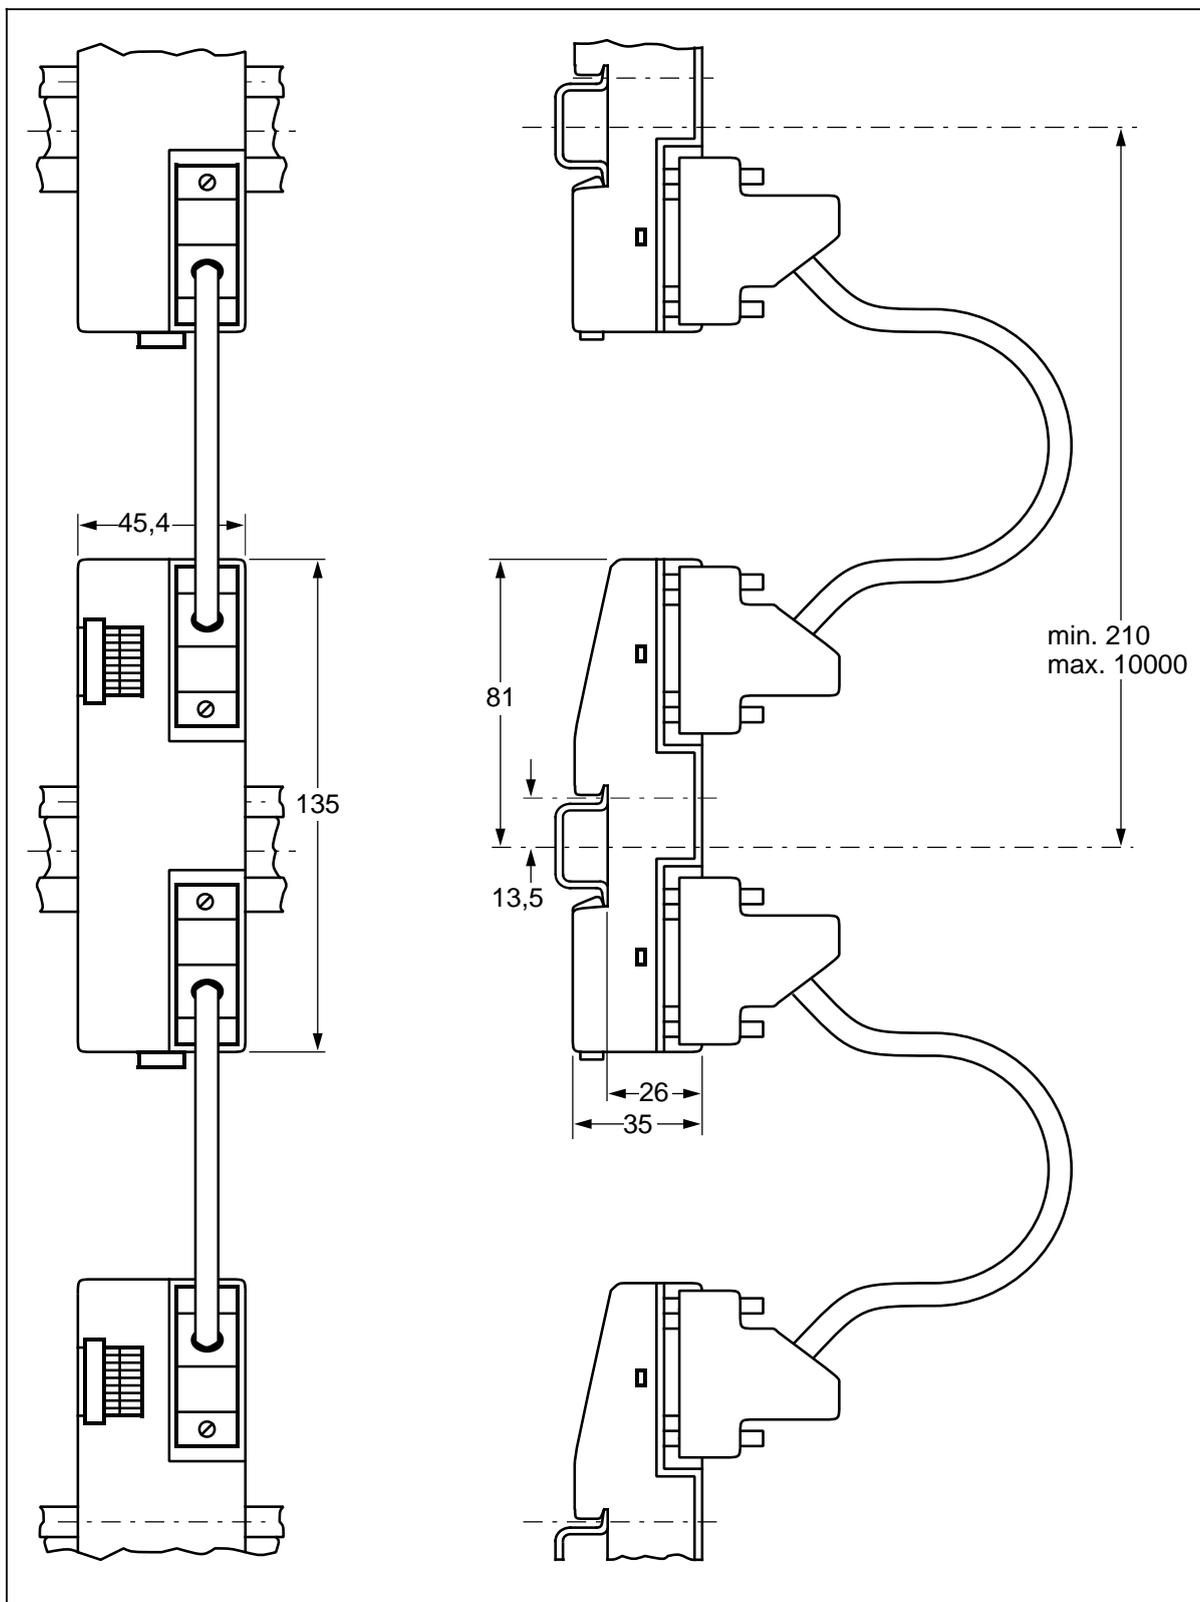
Maßbild der Anschaltungsbaugruppe IM 316 (6ES5 316-8MA12)
